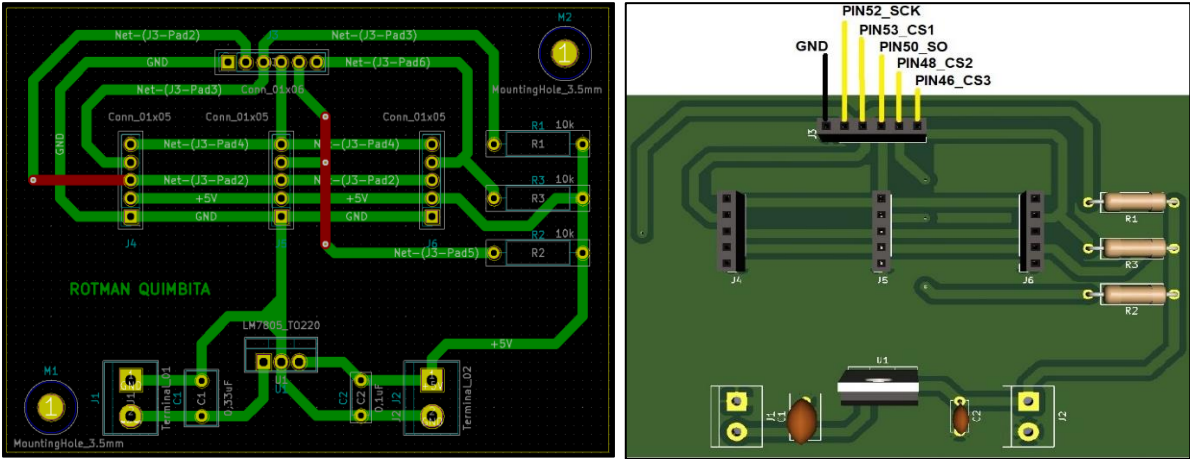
Módulo sensores de temperatura - diseño PCB y visualización 3D.
